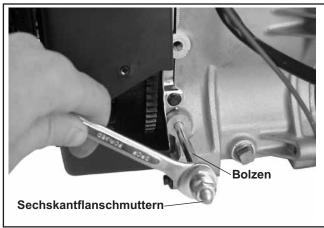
Entfernen der Befestigungsbolzen.
